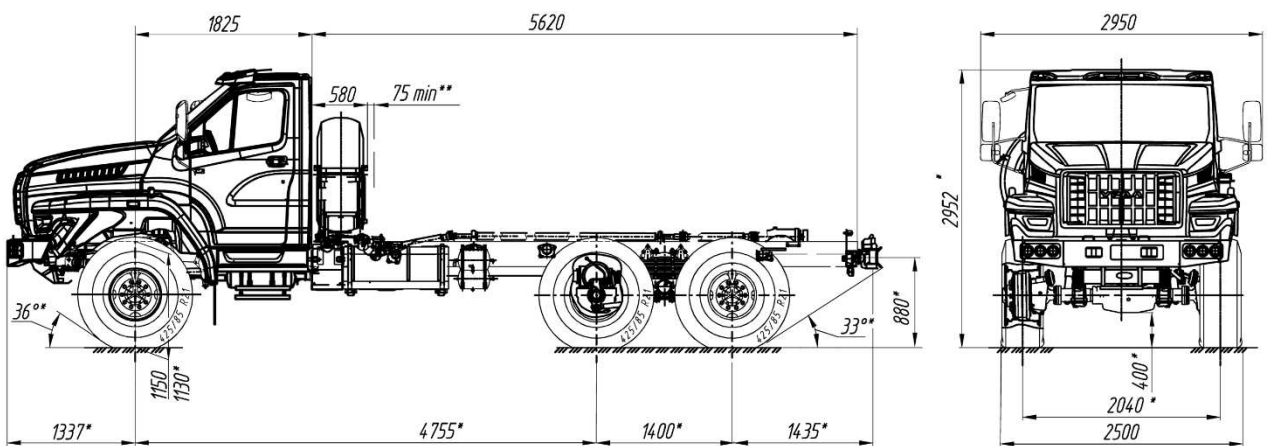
Габаритные размеры шасси Урал-4320-6951-72/74
